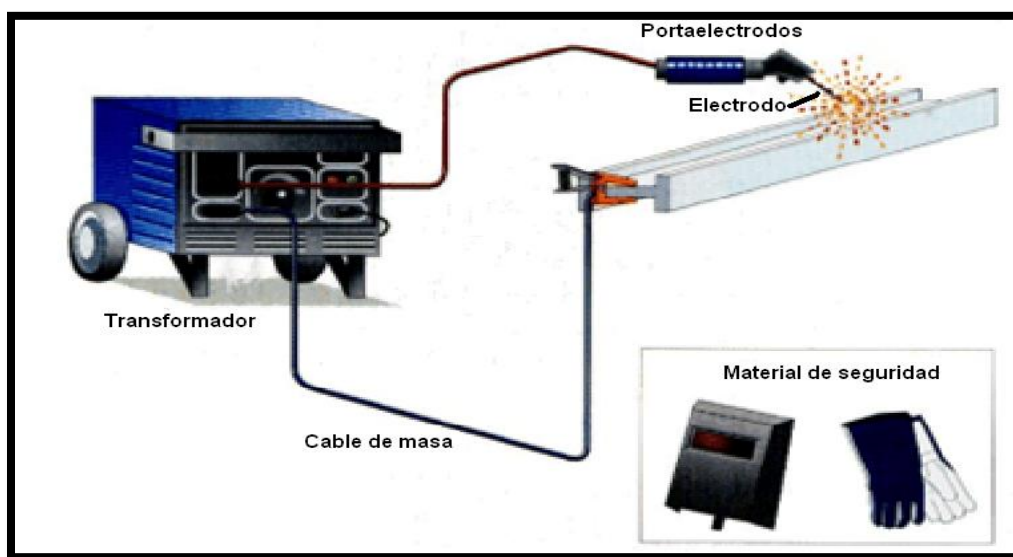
Partes del circuito de soldadura por Arco eléctrico
